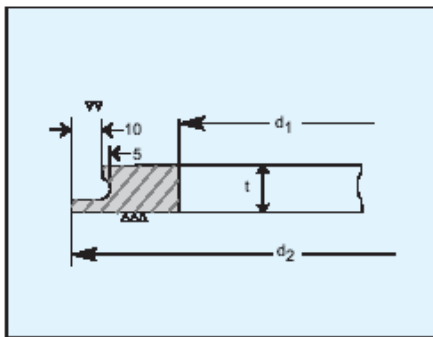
Juntas de sellado de membrana de soldadura.
